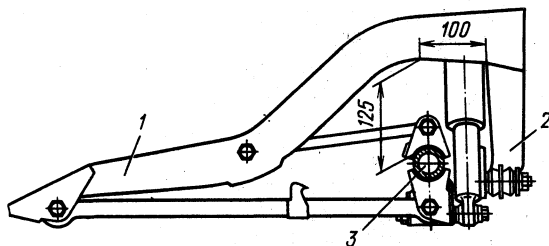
Установка задней подвески автомобиля «Жигули»:
